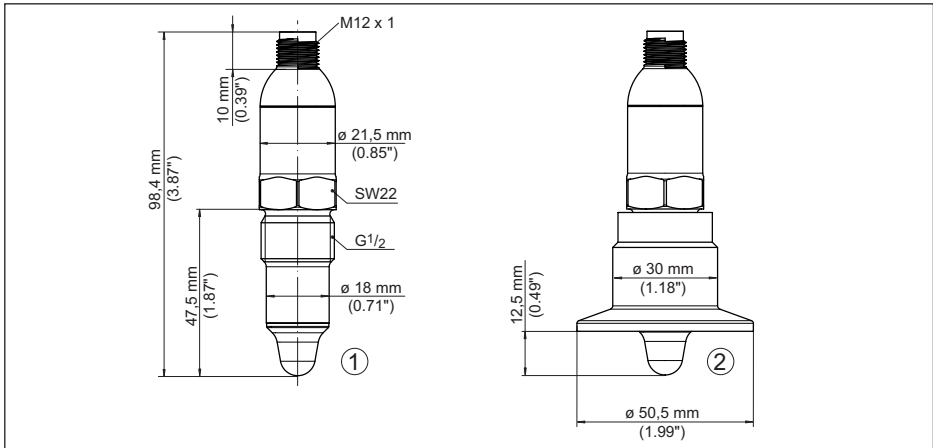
VEGAPOINT 11, Hygieneausführung - Gewinde
